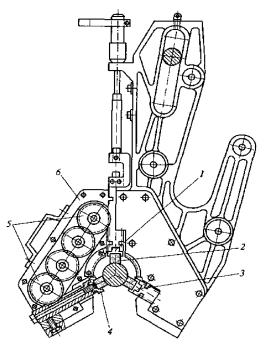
Головка для микрофиниширования: 1 – державка; 2 – брусок; 3, 4 – нижние державки; 5 – шестеренно-реечный механизм; 6 – корпус головки
